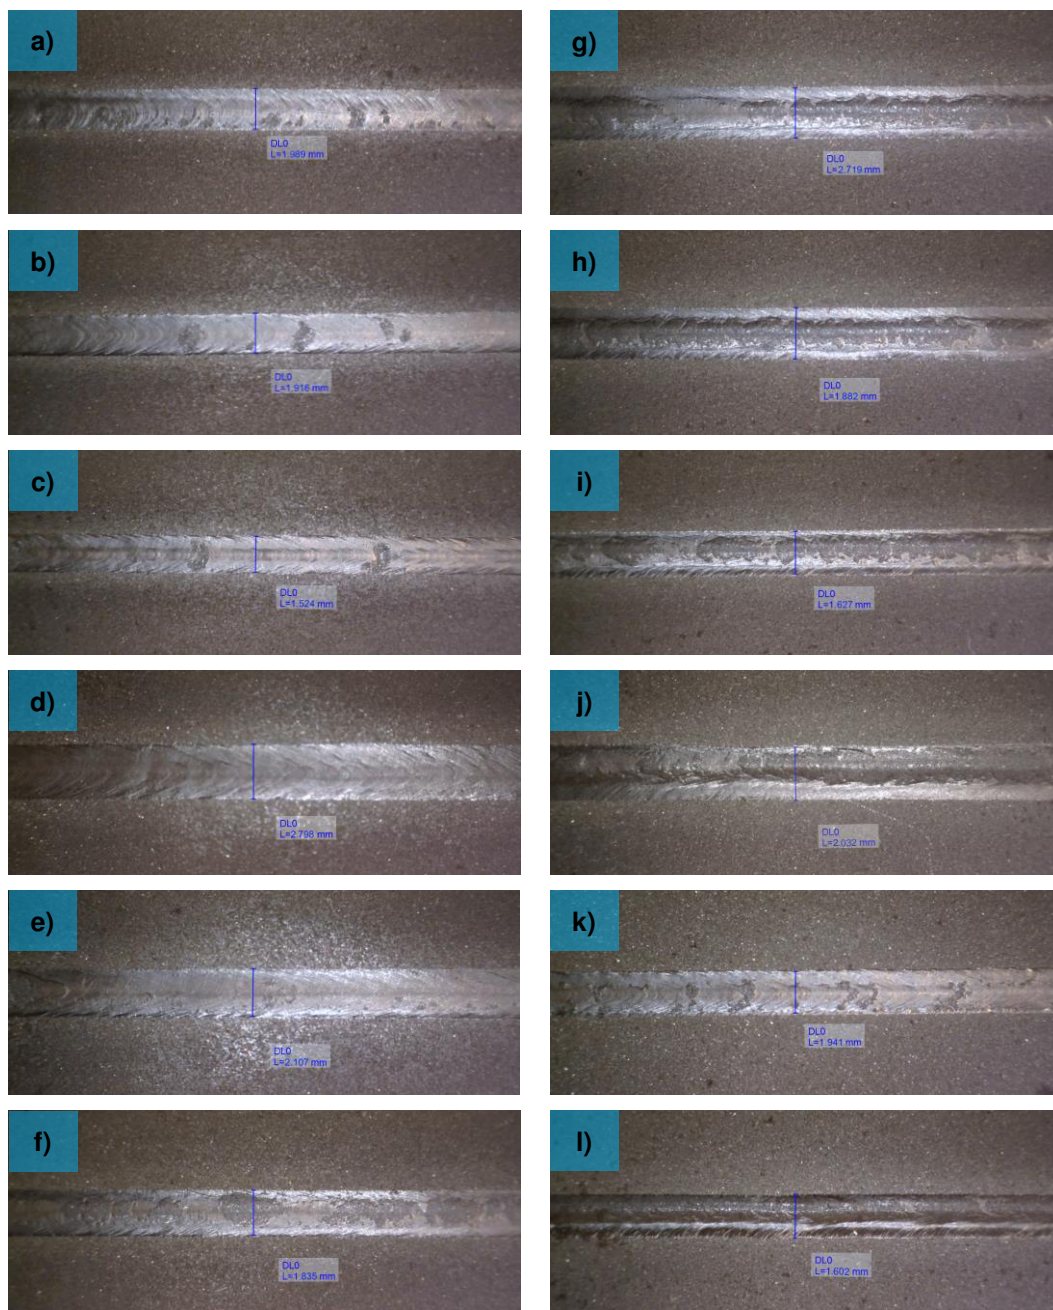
Cordones de soldadura del acero 22MnB5.
